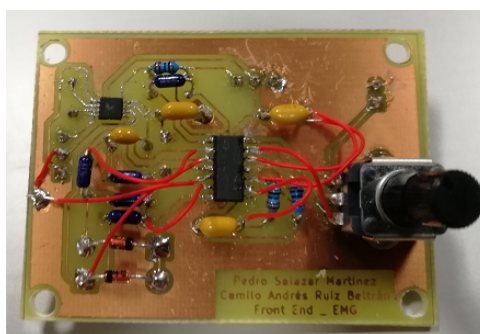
PCB con los reajustes y nuevas soldaduras mediante cables
